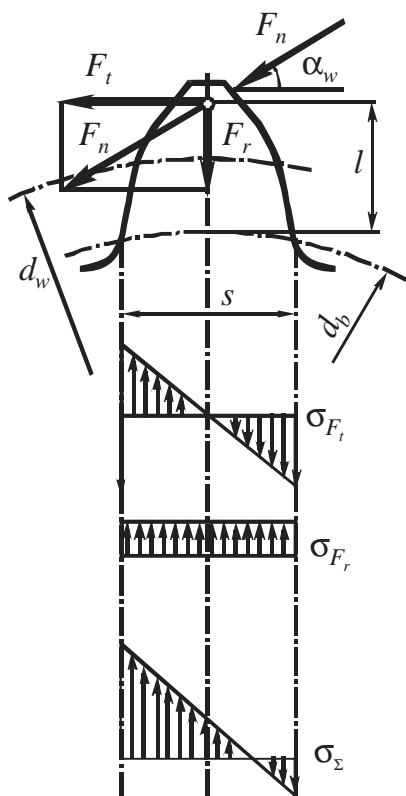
Напряжения изгиба при нагружения зуба зубчатого колеса
